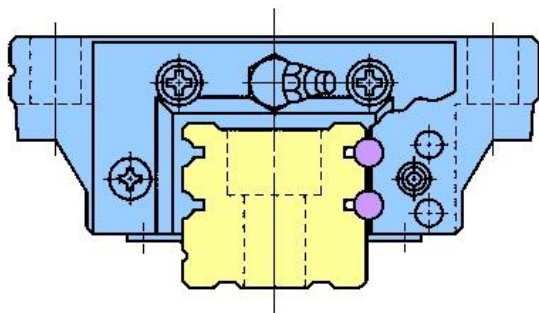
Druhy vedení CNC obráběcích strojů [6]
